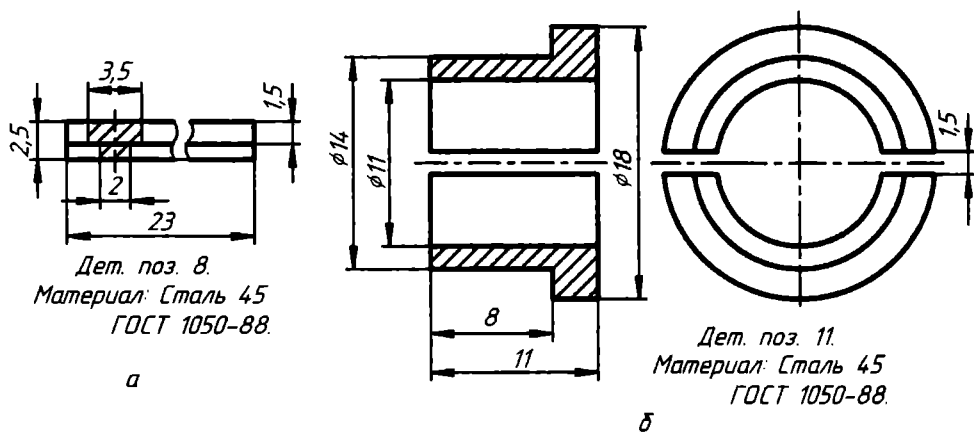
Чертежи: а — бруска; б — вкладыша
